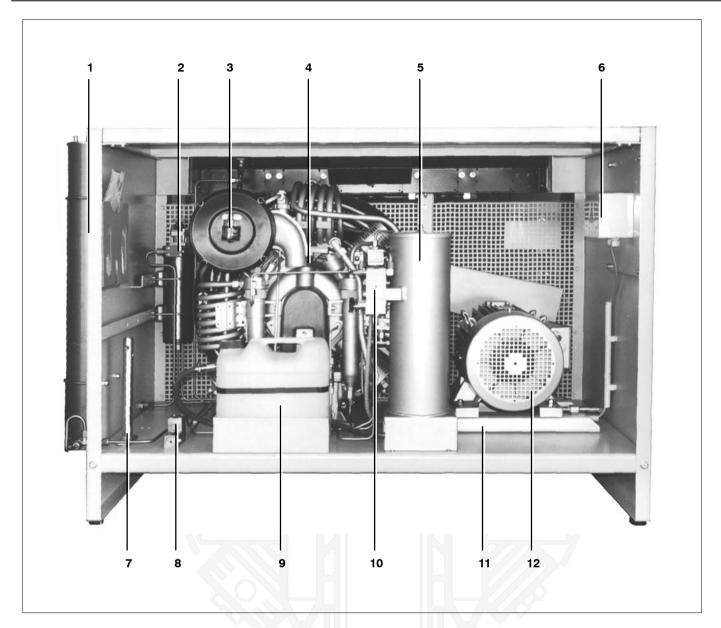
Groupe compresseur KAP 180-20, vue de face
